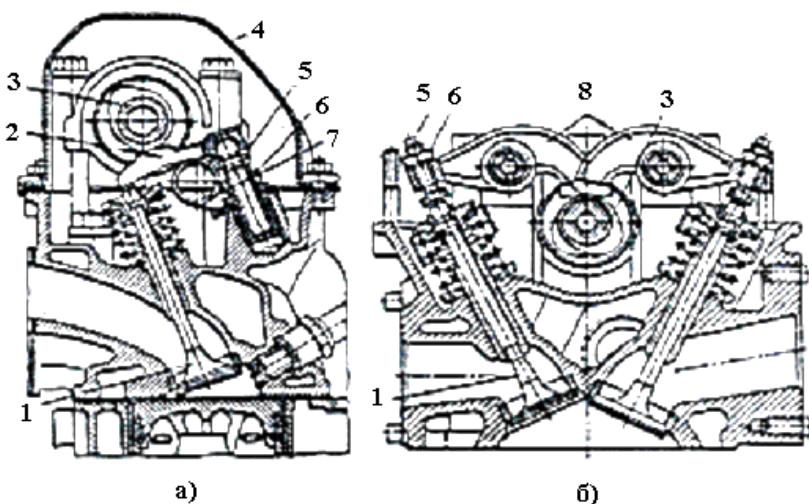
Схема газорозподільного механізму двигуна при розташуванні розподільного вала зверху
